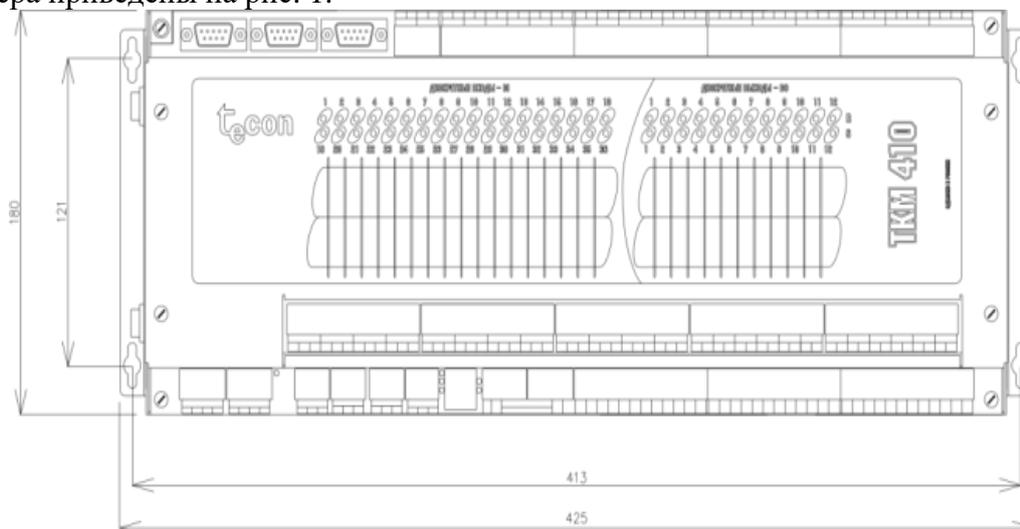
Габаритно-присоединительные размеры контроллера ТКМ410
